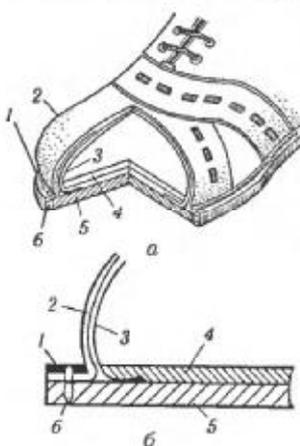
Допельне кріплення: *a* — розріз взуття; *b* — схема кріплення; 1 — рант; 2 — заготівка; 3 — підкладка; 4 — устілка; 5 — підшва; 6 — нитковий шов
